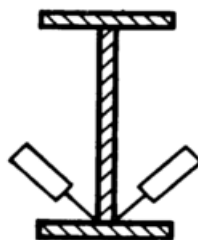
Положение электродов при сварке на универсальном стане
